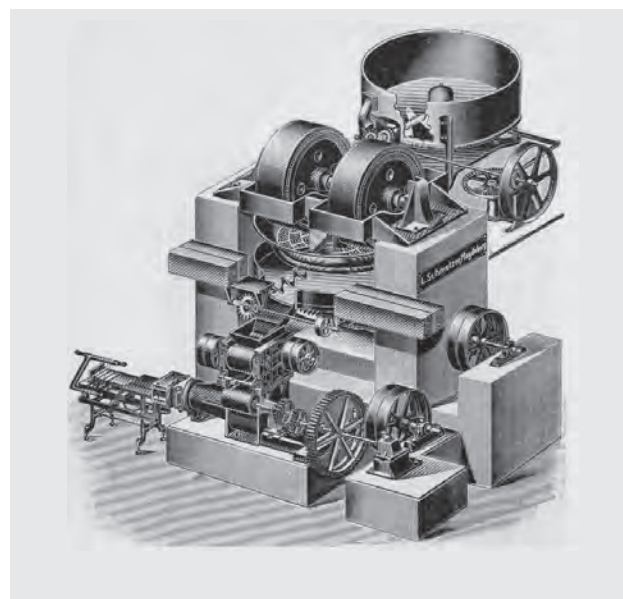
Aufbereitungsanlage von L. Schmelzer/Magdeburg mit Rundbeschicker, Kollergang, Sammelteller mit Austragschnecke, Walzwerk und Strangpresse, um 1914
